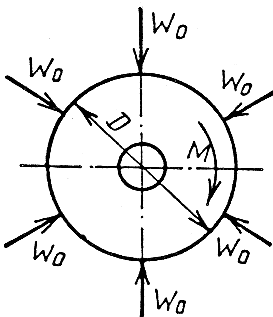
Сила зажима коротких деталей. Рисунок 3.17 - Клиновой привод приспособления.
